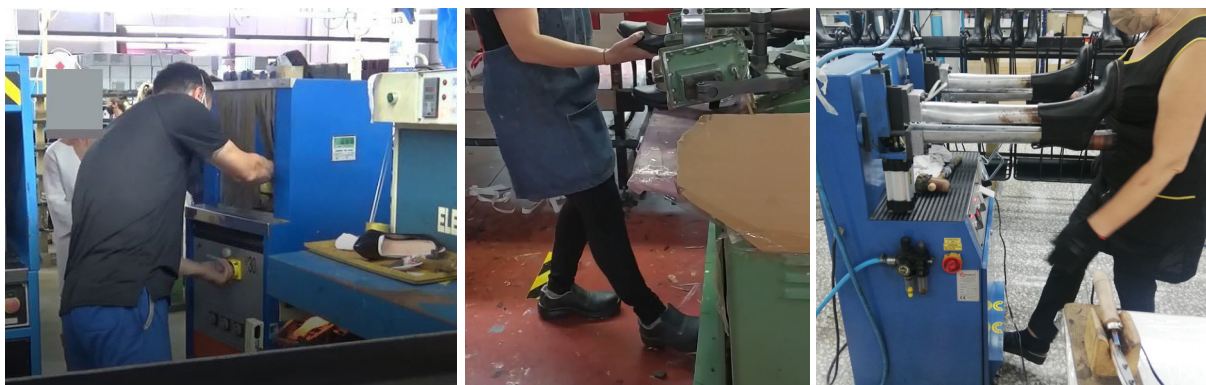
Adopción de posturas inadecuadas durante el accionamiento de mandos y pedales en máquinas del sector. Fuente: estudio de campo.
